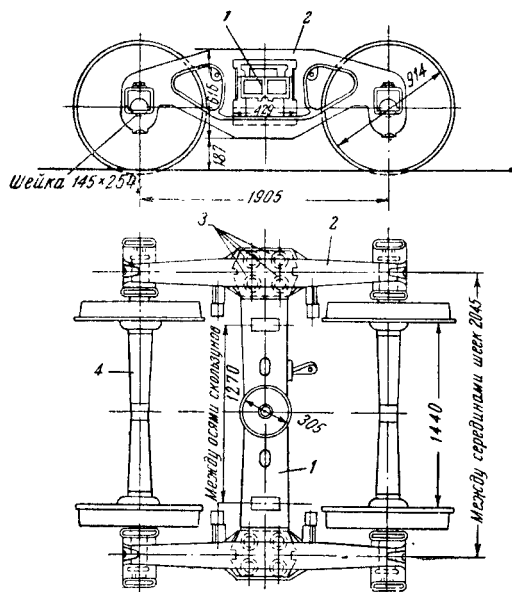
Тележка тендера паровоза серии Л: 1 — шкворневая балка; 2 — боковая рама; 3 — комплект рессор; 4 — букса; 5 — колёсная пара; 6 — рычажная передача
